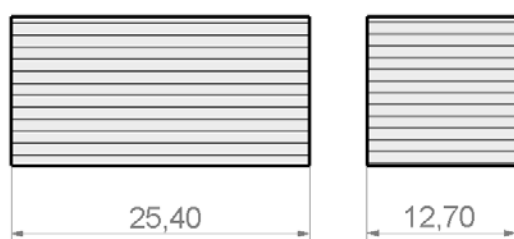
Esquema de la proveta curta de secció circular per l'assaig a compressió (mesures en mm)
